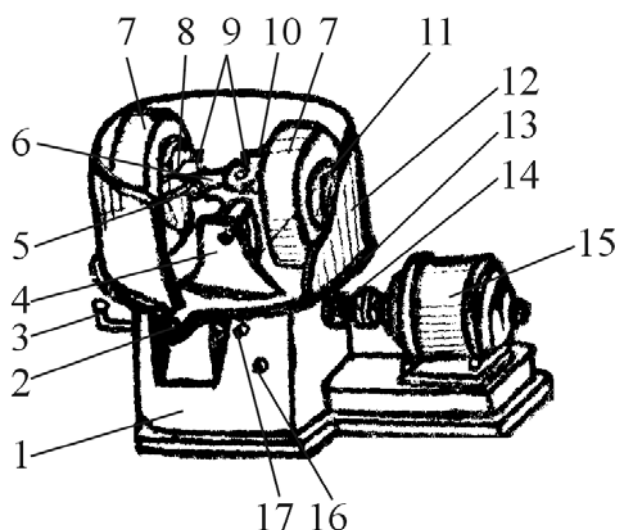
Схема лабораторного коткового змішувача моделі 018М: 1 – станина; 2 – заслінка; 3, 16 – трубки; 4, 10 – плужки; 5, 9 – регулювальні болти; 6 – траверса; 7 – котки; 8 – вісь; 11, 14 – вали; 12 – кожух; 13 – стіл; 15 – електродвигун; 17 – пробка
